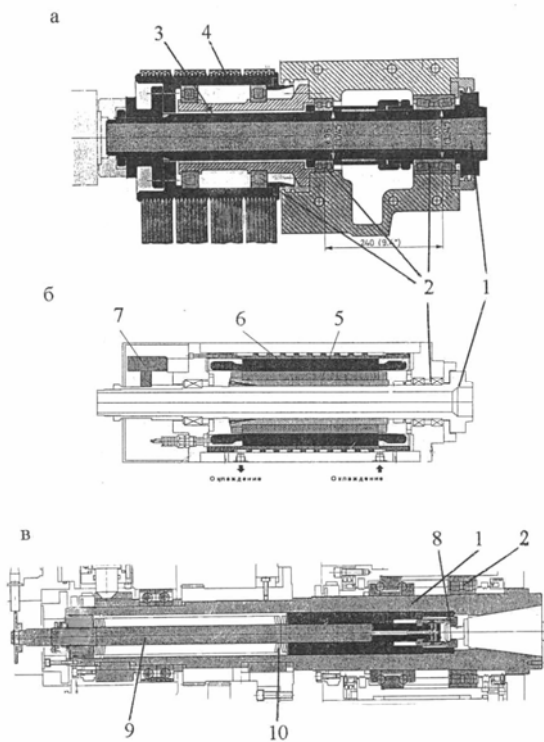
Варианты конструктивных схем шпиндельных узлов станков с ЧПУ: а – с разгрузкой шпинделя от изгибающего момента привода; б – двигатель-шпиндель; в – с устройством автоматического зажима-разжима инструмента; 1 – шпиндель; 2 – подшипники; 3 – опорный стакан; 4 – приводной шкив; 5 – ротор; 6 – статор; 7 – датчик; 8 – цапга зажима инструмента; 9 – толкатель; 10 – тарельчатые пружины
